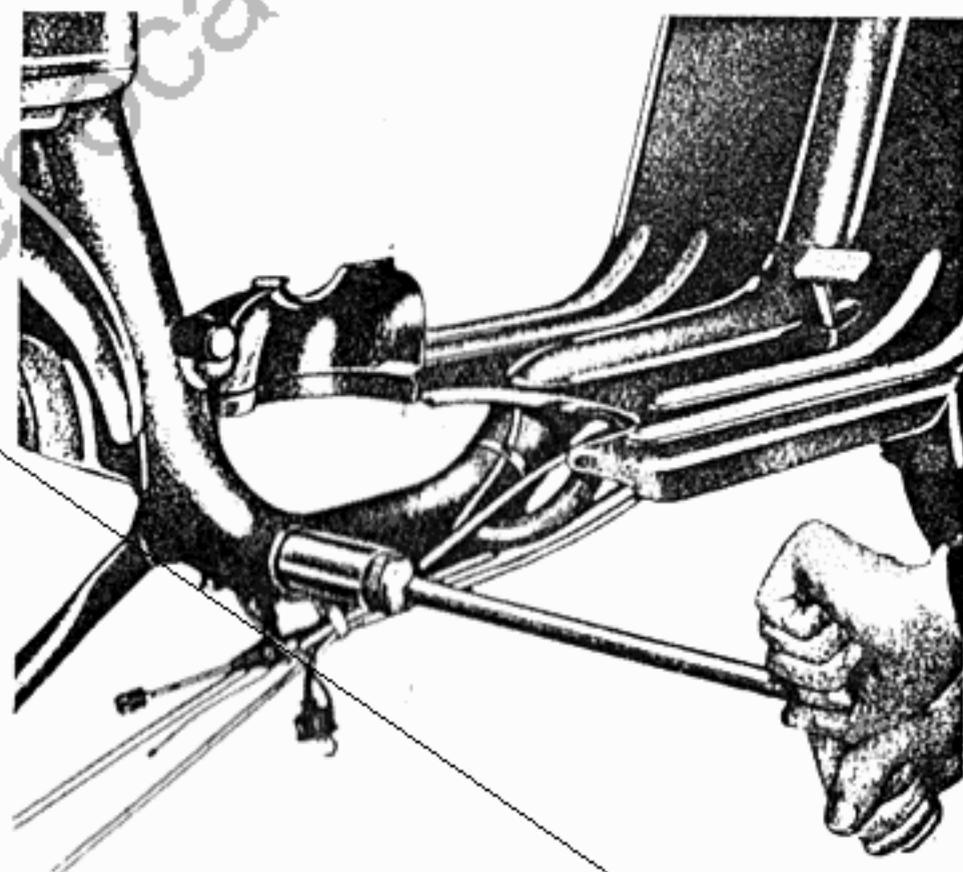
Smontaggio canotto rotazione motore dal telaio
